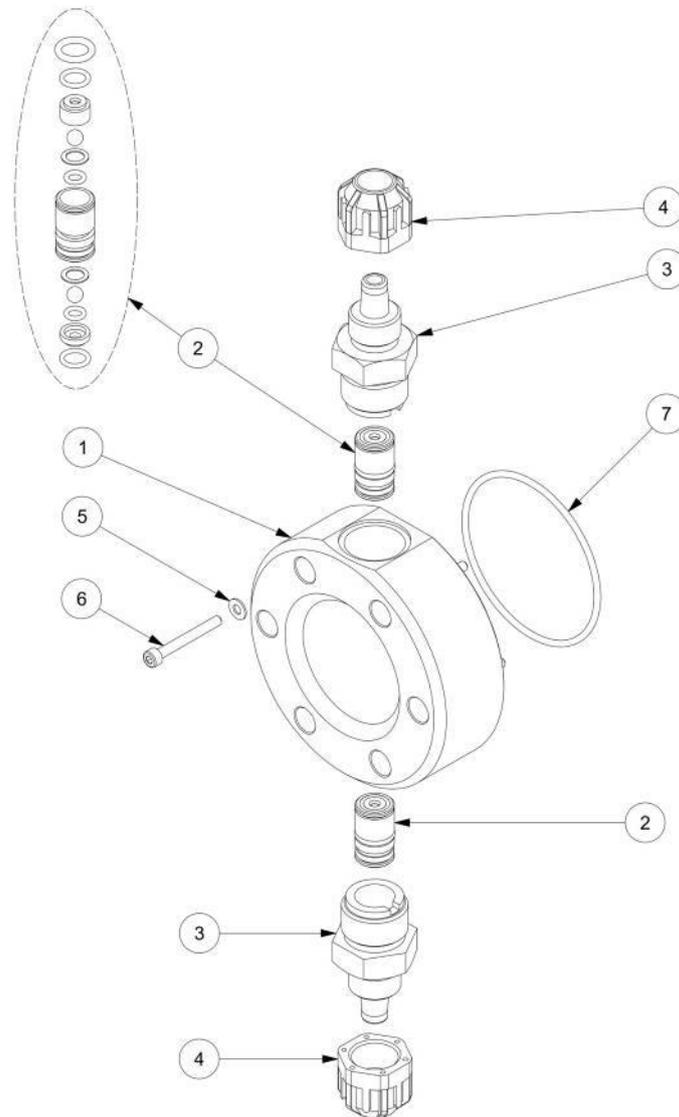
HC899 - Corpo pompa valvole a labbro e sfera / Pump head lip and ball valves / Corps pompe et clapets à lèvres et bille / Cuerpo de la bomba valvulas a labio y a esfera / Pumpenkörper Lippen- und Kugelventile / Головка насоса, губчатый и шариковый клапан
